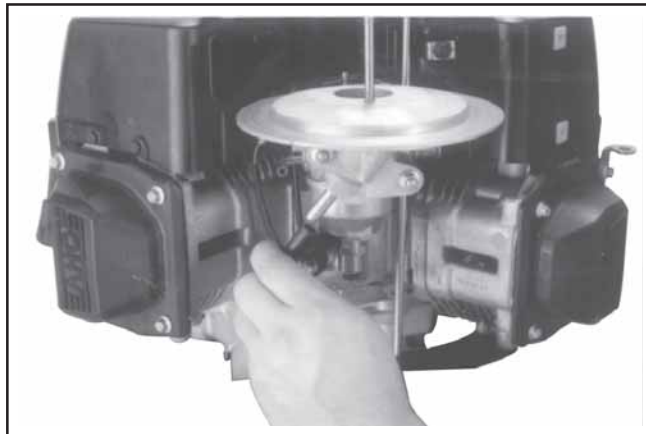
Installazione del tubo del carburante (Commercial Mower).
